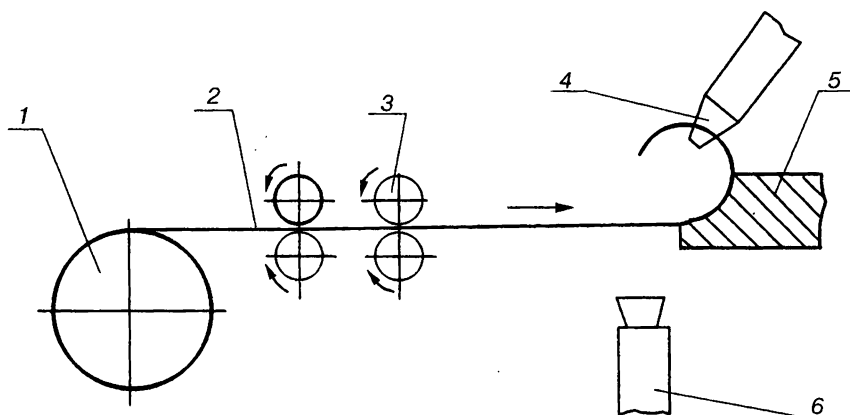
Схема безоправочной навивки пружин на станках-автоматах:
